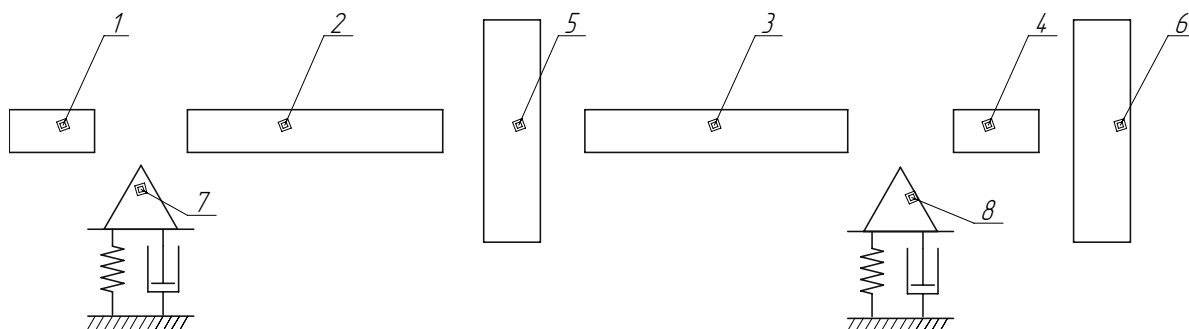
Расчетная схема шпиндельного узла с приспособлением, где 1, 2, 3, 4 –участки шпиндельного узла; 5 – зубчатое колесо, через которое передается вращение на шпиндель; 6 – приспособление; 7, 8 – подшипниковые опоры
